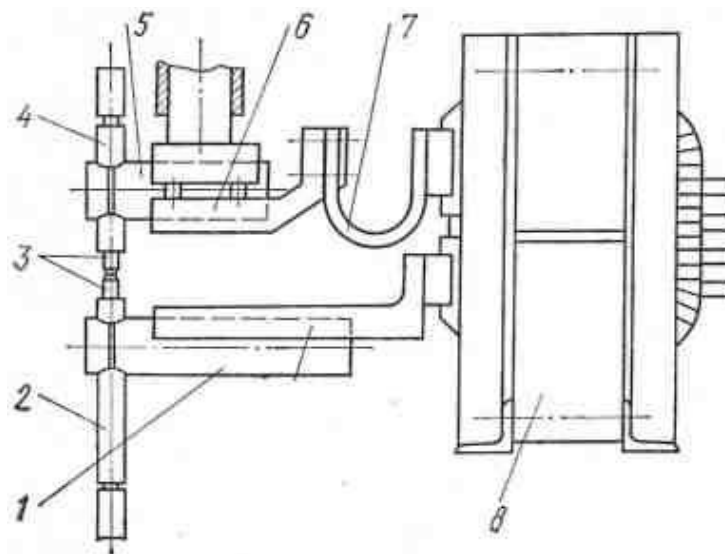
Сварочный контур машины для точечной сварки
